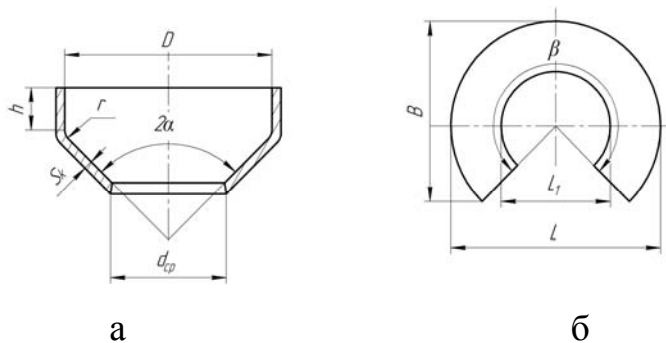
Схема конічного невідбортованого днища: а – головний вигляд; б – розгортка
